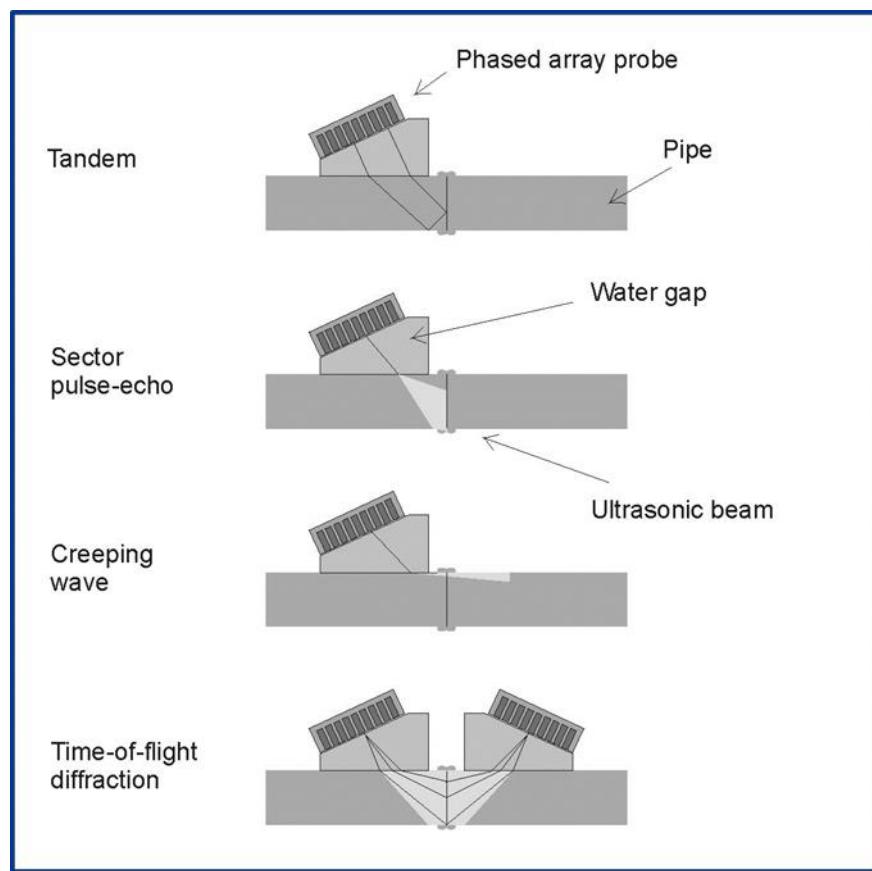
Esquema de diferentes técnicas de inspección de soldaduras a tope
